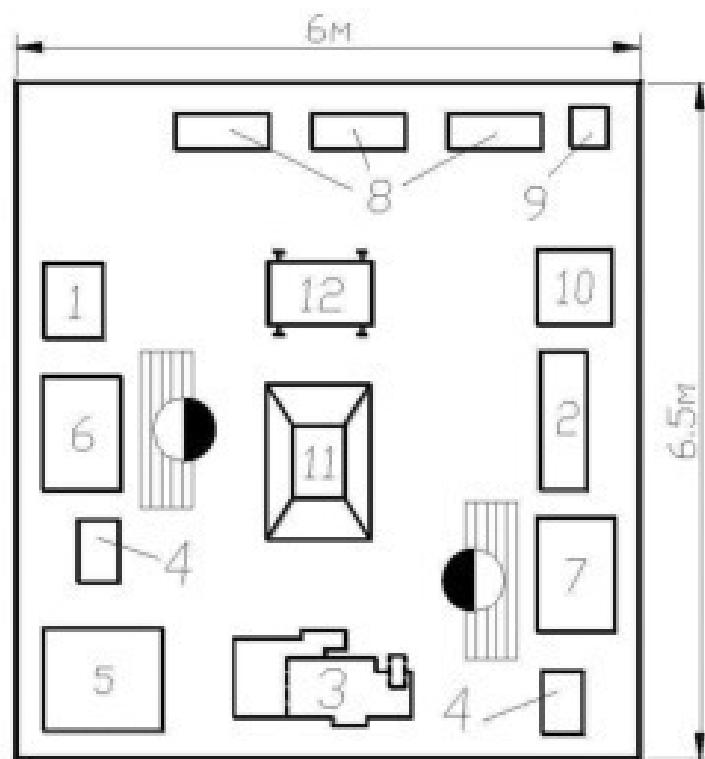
Планировка сварочно-наплавочного отделения.
